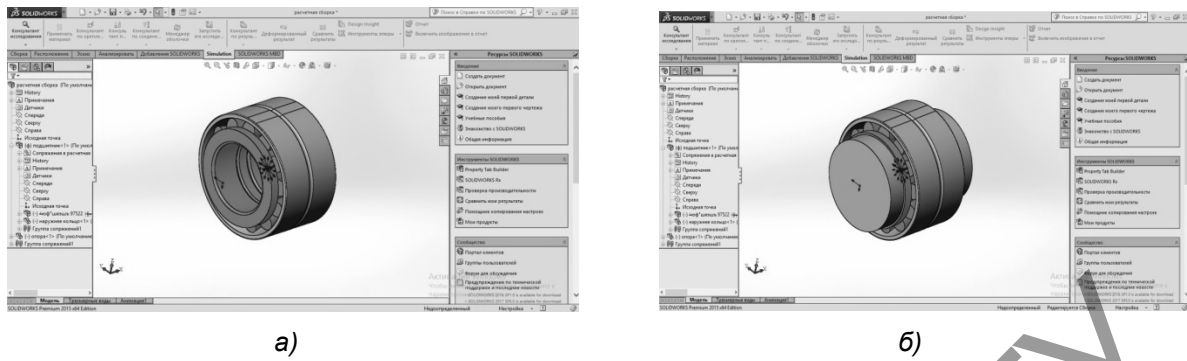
Расчетная схема для определения перемещений в SolidWorks: двухрядный радиальный подшипник (а); сборка подшипниковой опоры (б)
